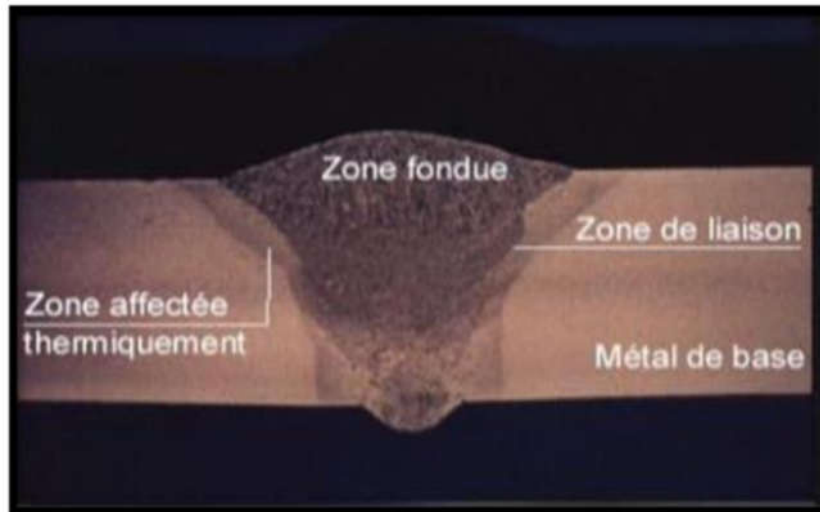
Présentation macrographique d'un joint soudé [15]
